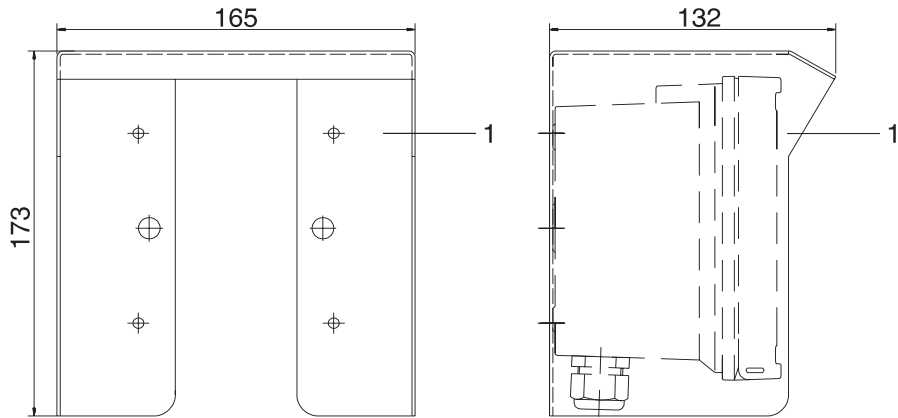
Tampa protetora ZU 0276 para montagem em parede e tubulação
